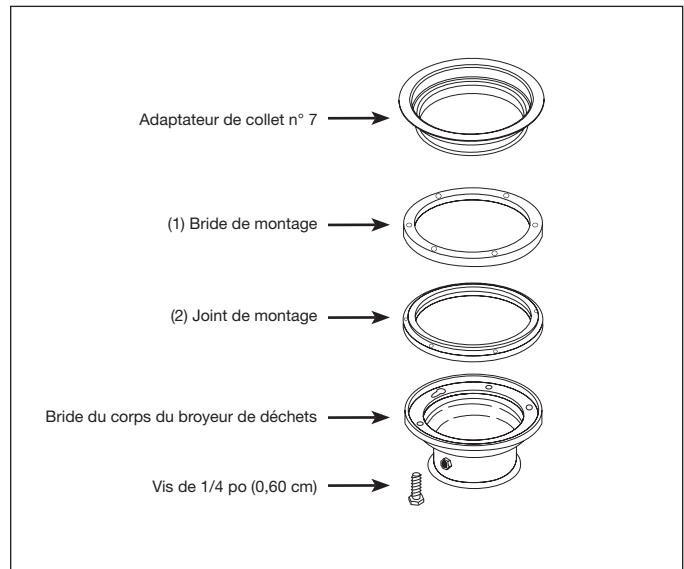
Ensemble de montage n° 7 ou de bol d'évier
